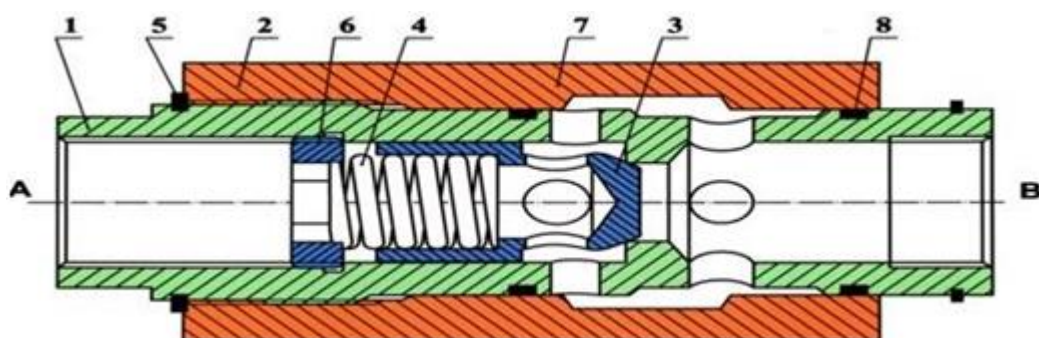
Принцип действия дросселя с обратным клапаном для трубного монтажа: 1 – внутренний корпус; 2 – поворотный корпус; 3 - седло; 4 – пружина; 5 – запорное кольцо; 6 – упорная шайба; 7 – наружный корпус; 8 – резиновое кольцо; А – отвод (выход); В – подвод (вход).
